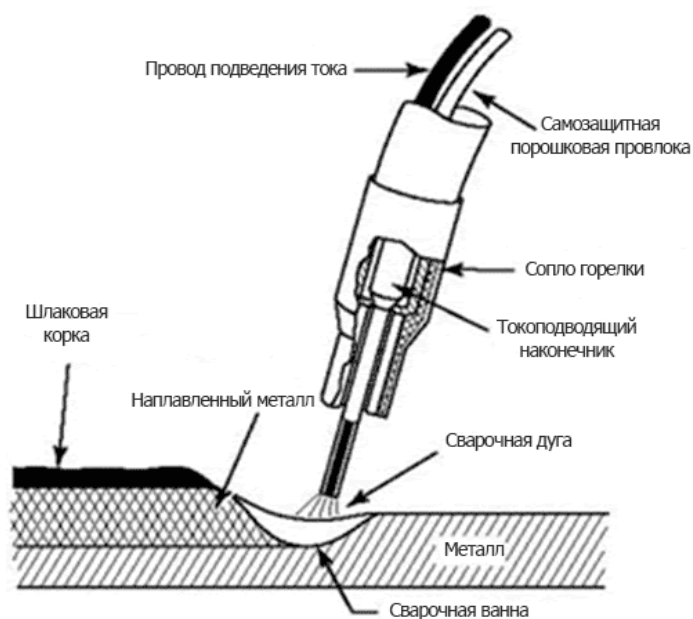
Схема выполнения сварки порошковой самозащитной проволокой
